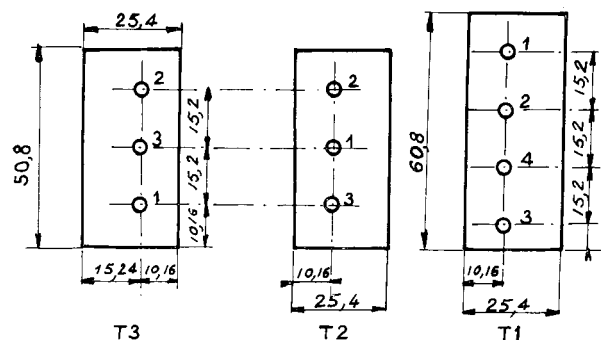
Dessin des plaquettes supportant les bobinages (vue de dessus)
